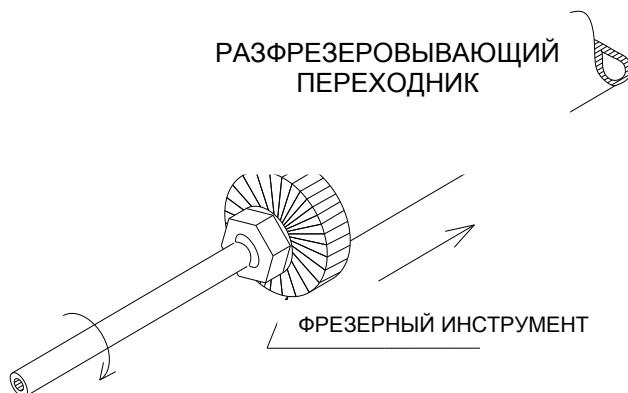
Торцовка посадочных поверхностей на наварных деталях
